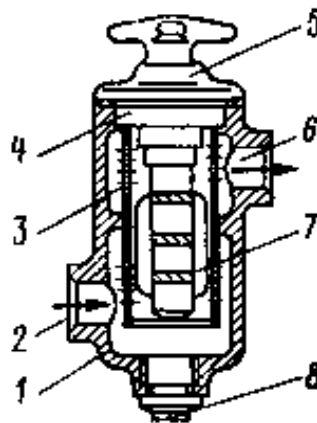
Магнітний фільтр: 1 – корпус; 2 – вхідний патрубок; 3 – сітка; 4 – магніт; 5 – кришка; 6 – вихідний патрубок; 7 – ребро; 8 – пробка
